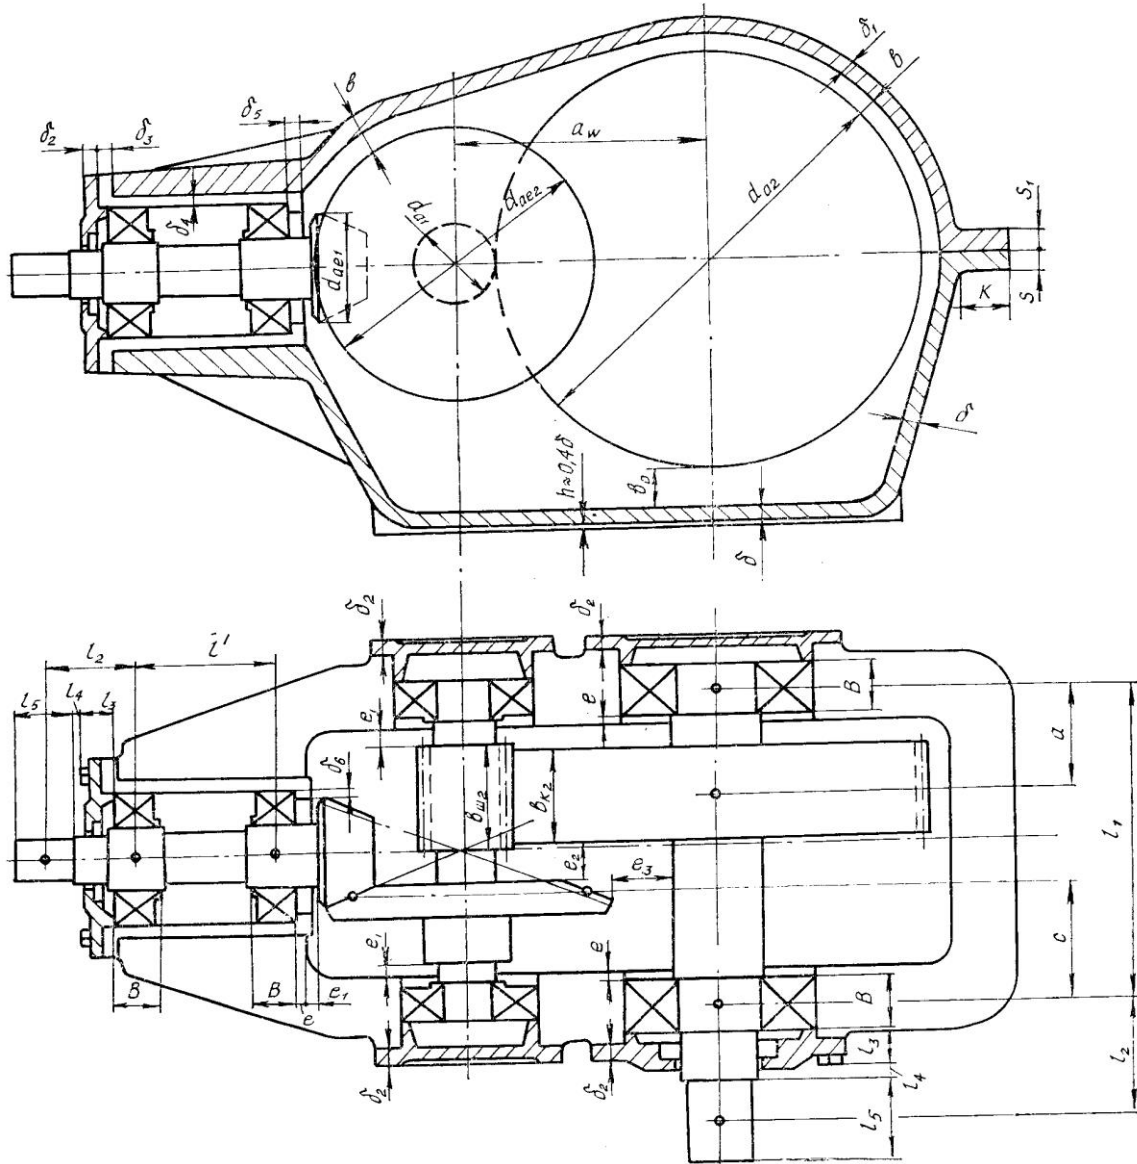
Компонувальне креслення конічно-циліндричного редуктора
